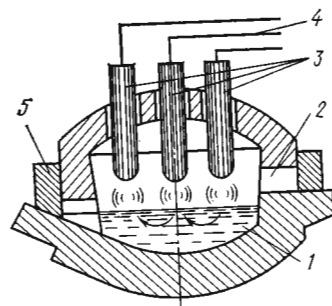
Схема трехфазной дуговой электропечи для плавки стали:
